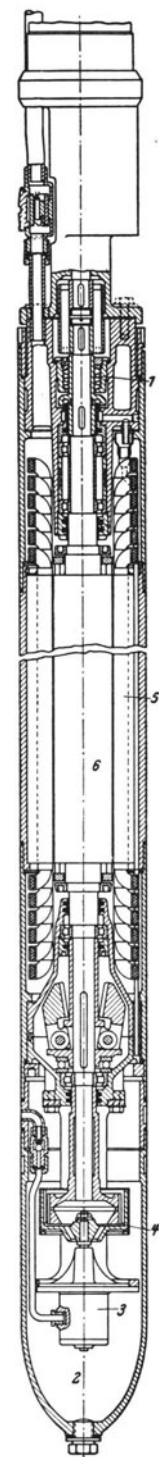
Schnitt durch den Motor der Elmo-Tiefbrunnenpumpe „Motor unten“.
